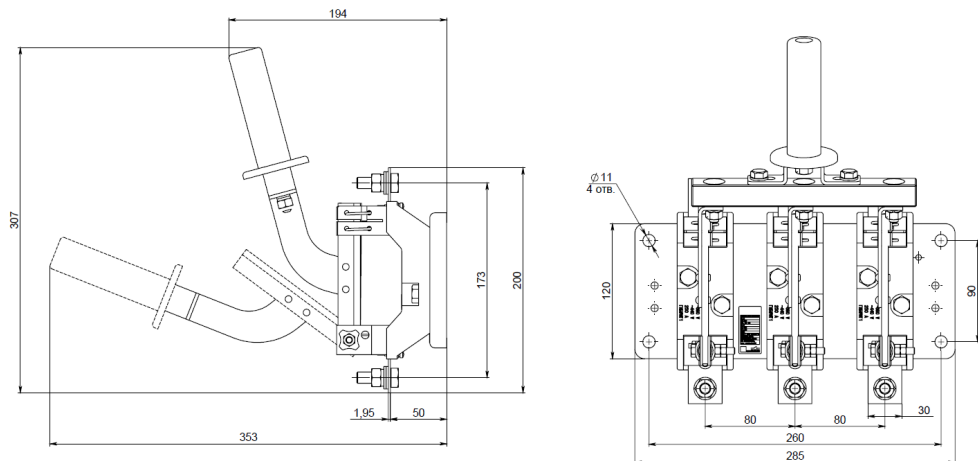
Разъединитель РЕ19-31(35)-31120-00 УХЛ3 трехполюсный с боковой рукояткой, масса 3,57 кг
